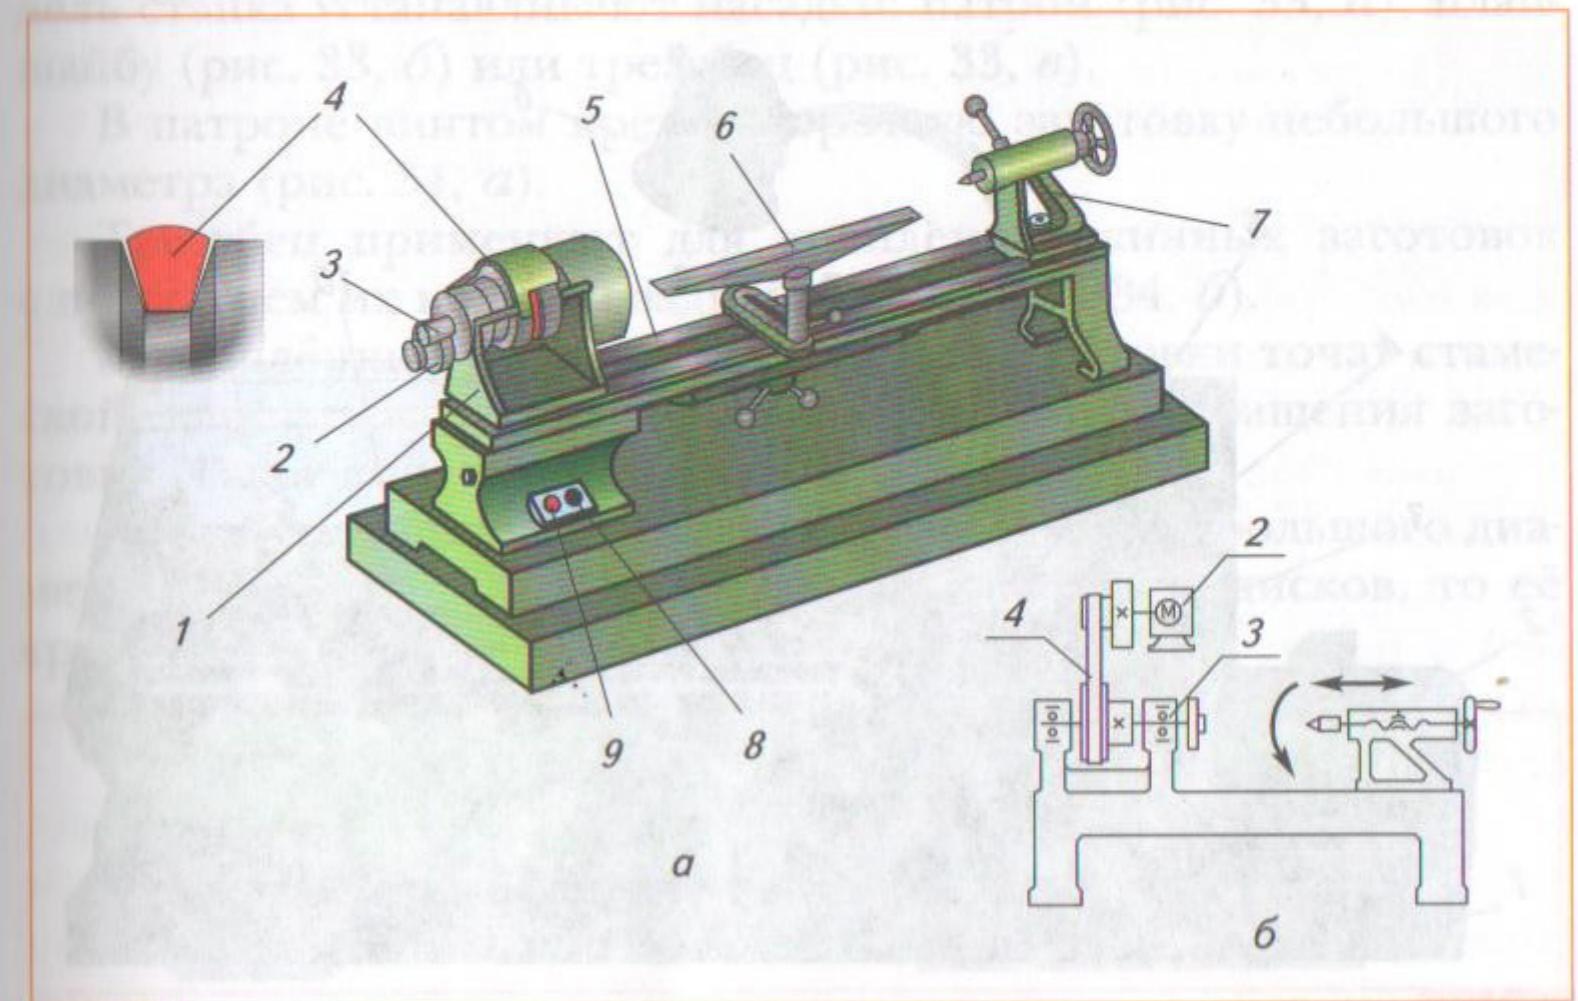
Токарный станок ТД-120 для точения древесины: а — общий вид; б — кинематическая схема; 1 — передняя бабка; 2 — электродвигатель; 3 — шпиндель; 4 — клиноремённая передача; 5 — направляющие; 6 — каретка с подручником; 7 — задняя бабка; 8 — кнопка «Пуск»; 9 — кнопка «Стоп»
